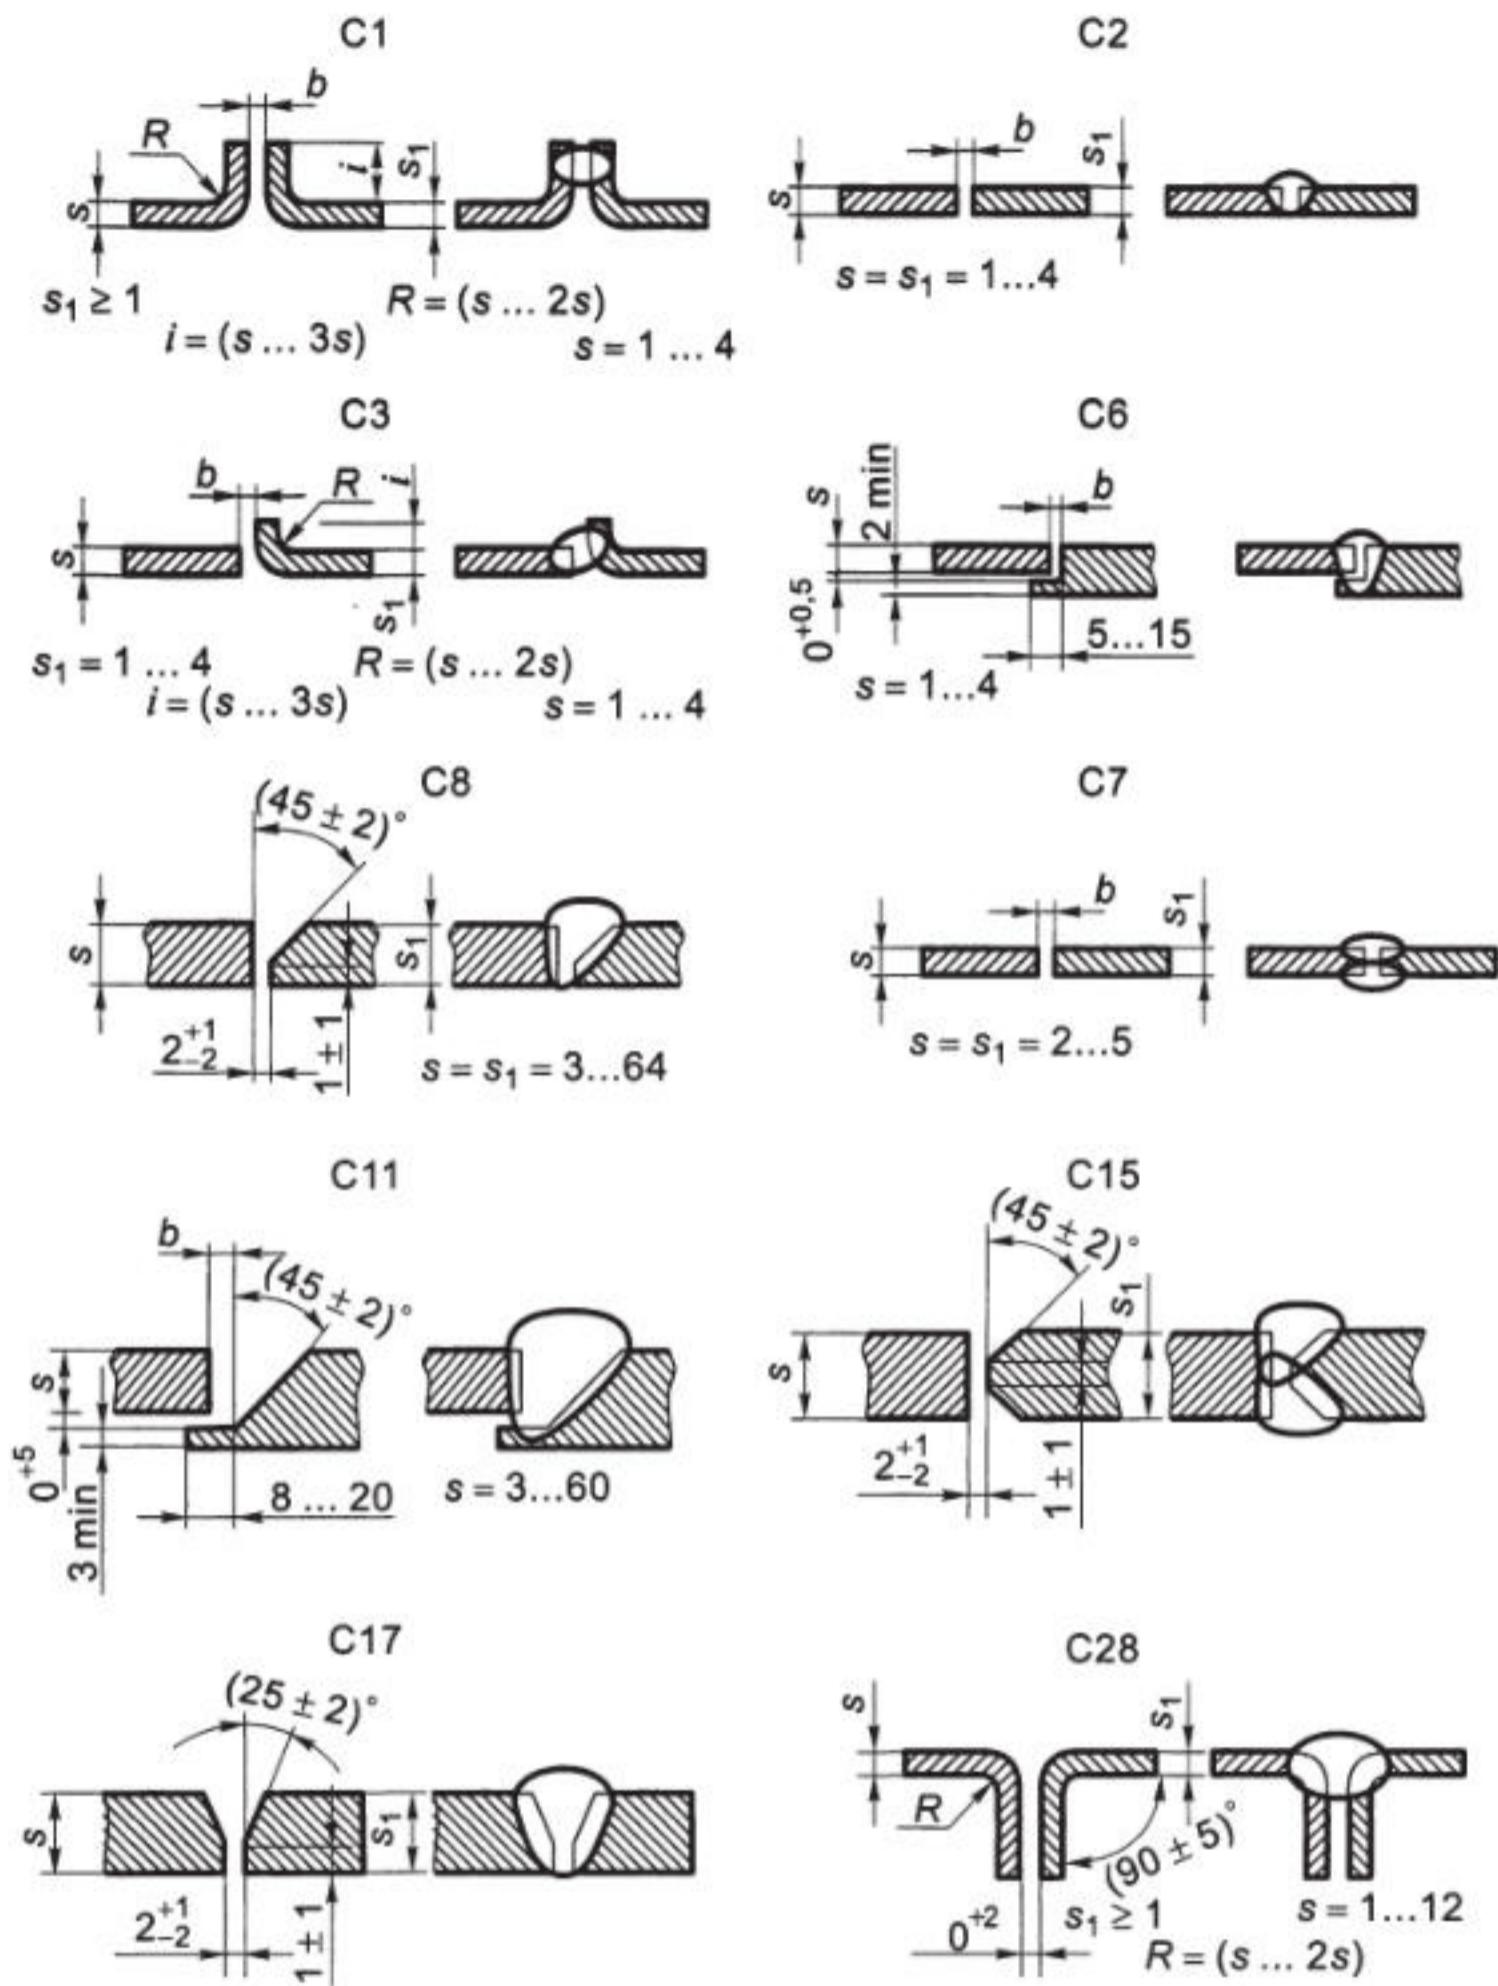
Стыковые сварные соединения: форма подготовленных кромок и сварного шва, их условные обозначения
